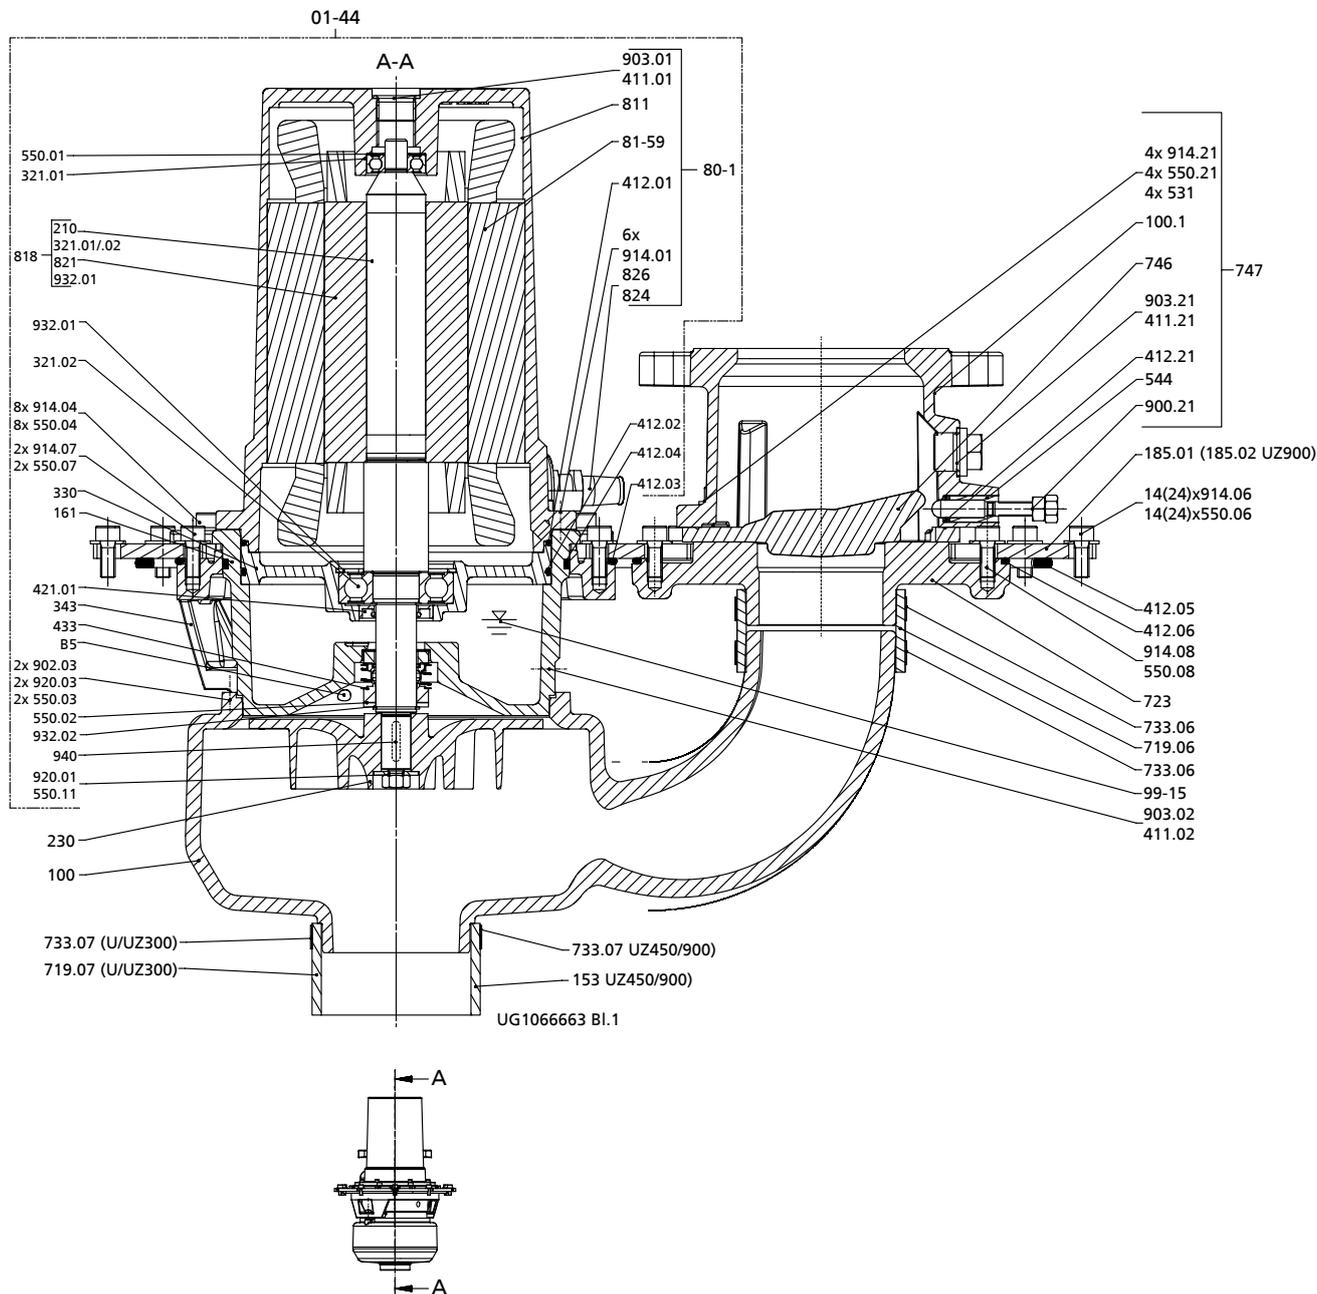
Сборочный чертеж Compacta U100/300, UZ150/300, UZ 450/900 — съемный узел
